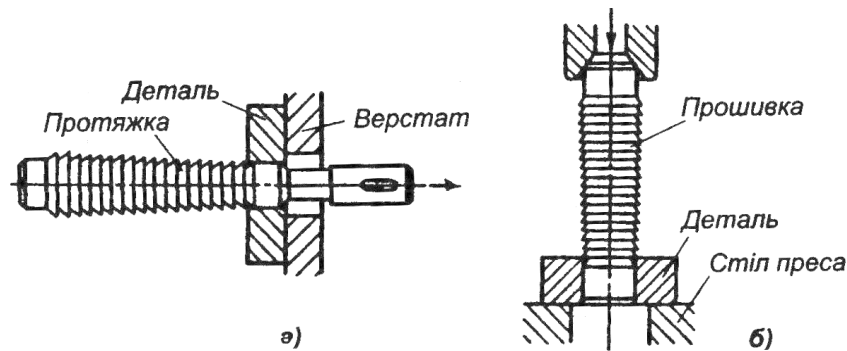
Схеми роботи: а) протяжки; б) прошивки
